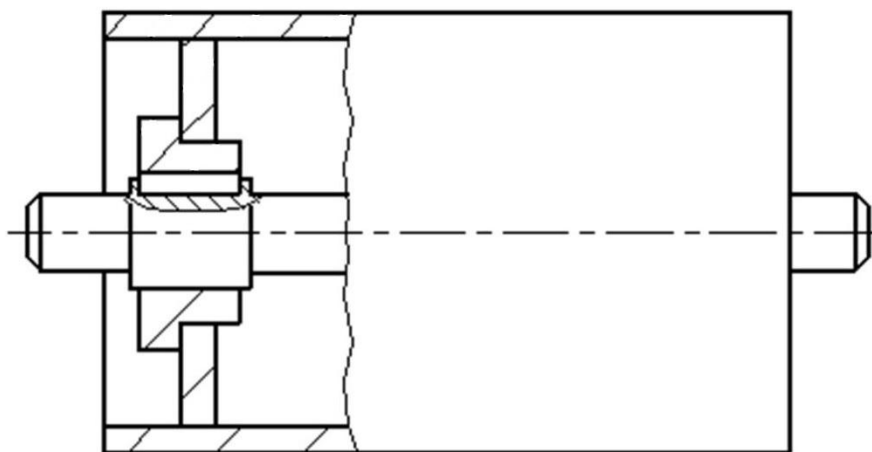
Пример изображения сварной сборочной единицы на сборочном чертеже изделия
